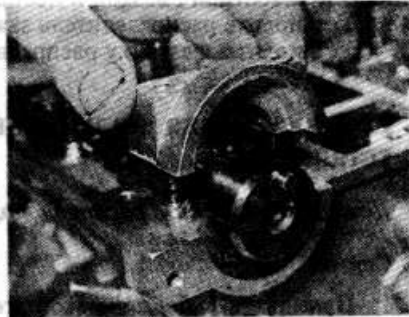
Снятие крышки подшипника распредвала — двигатель с двумя распредвалами
